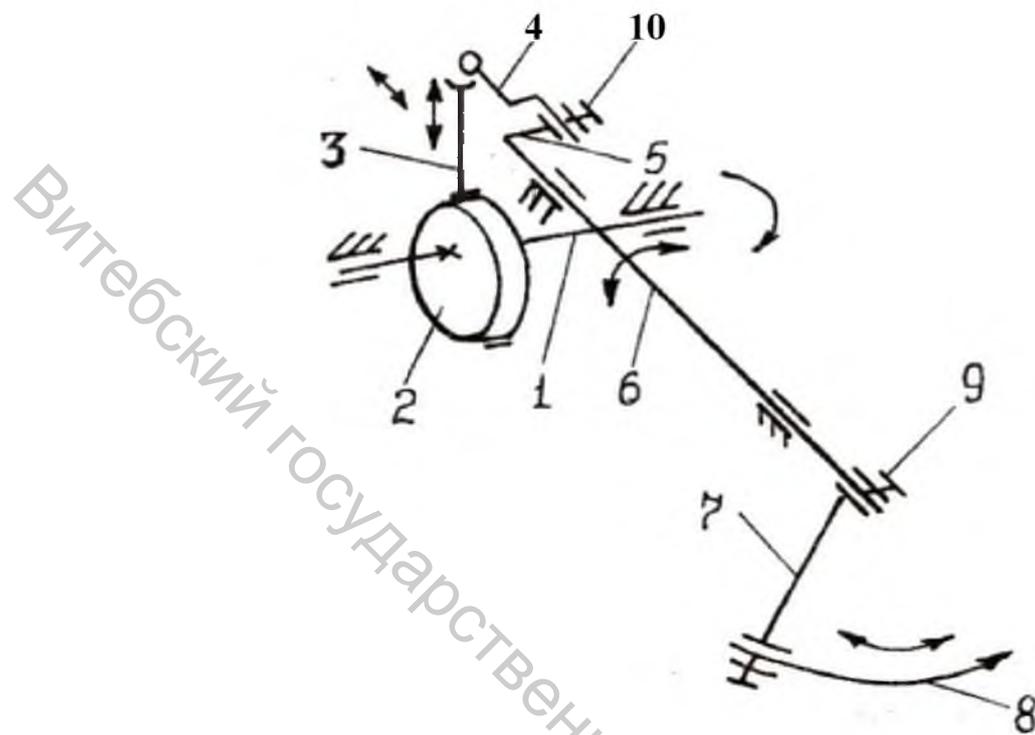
Кинематическая схема механизма иглы машины потайной строчки
